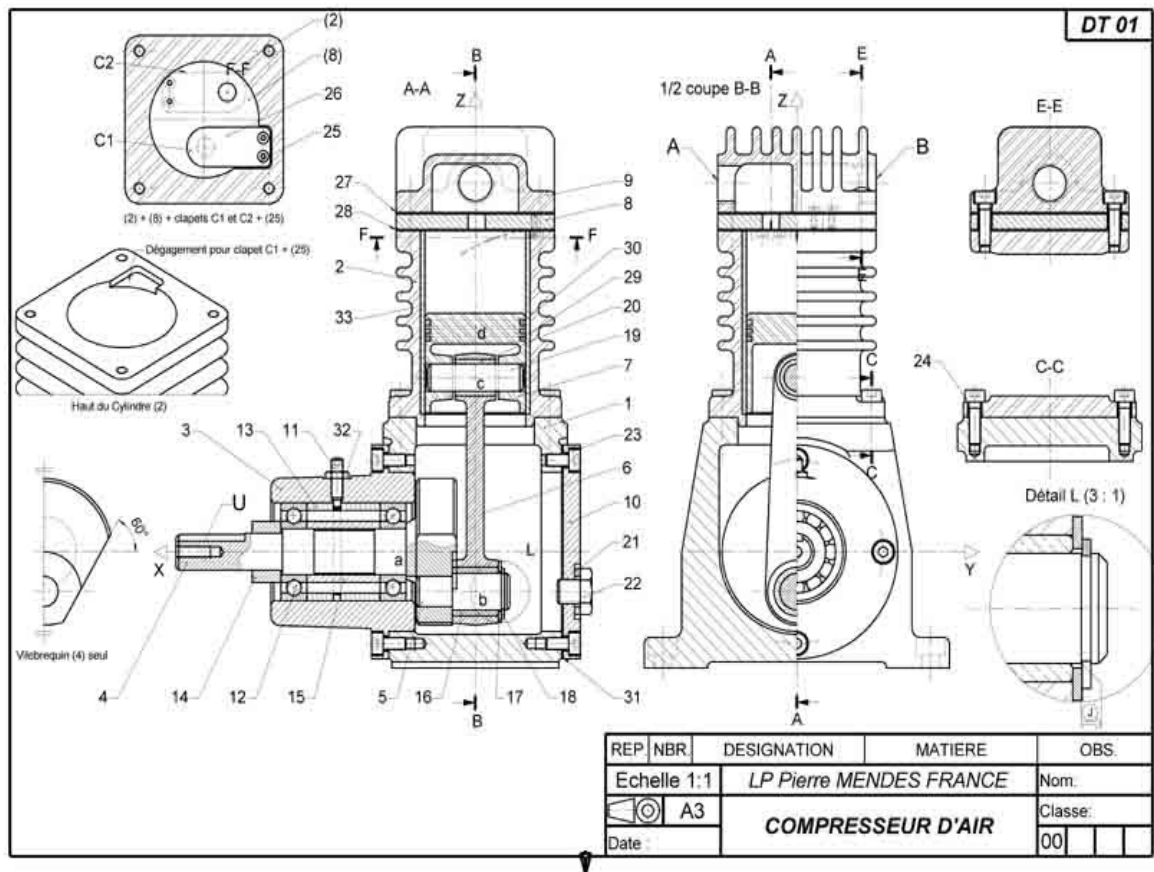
dessin d'ensemble d'un compresseur d'air
